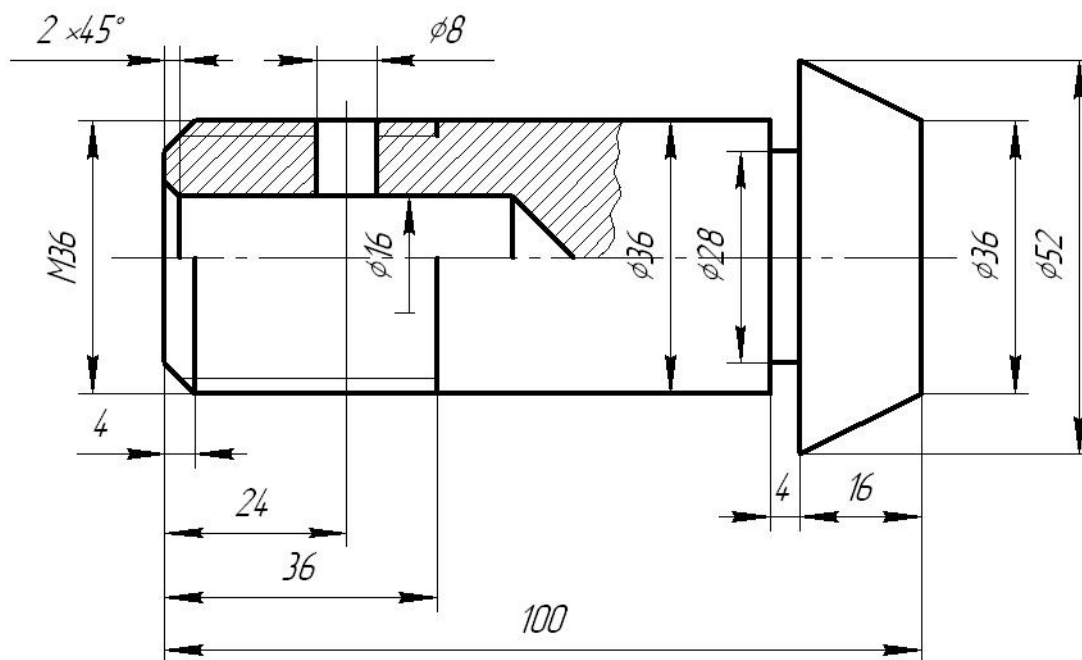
Чертеж детали с осевыми размерами (допуски на все конструкторские размеры должны быть известны)
